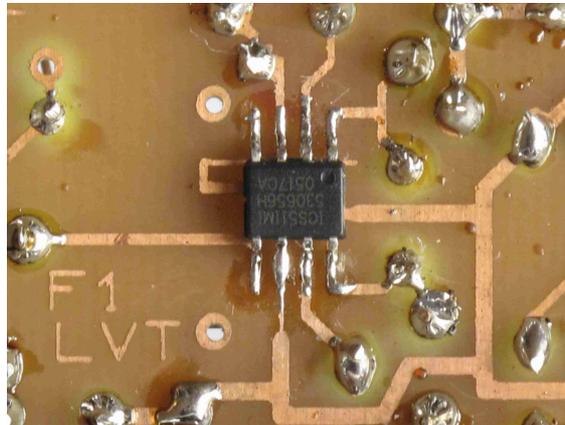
Circuit intégré ICS 511 soudé coté pistes cuivre sous le quartz.
